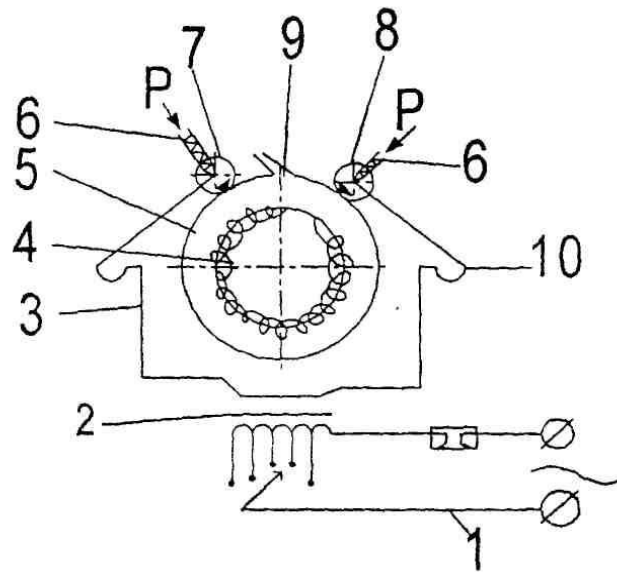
Схема установки для електроконтактною наплавлення:
